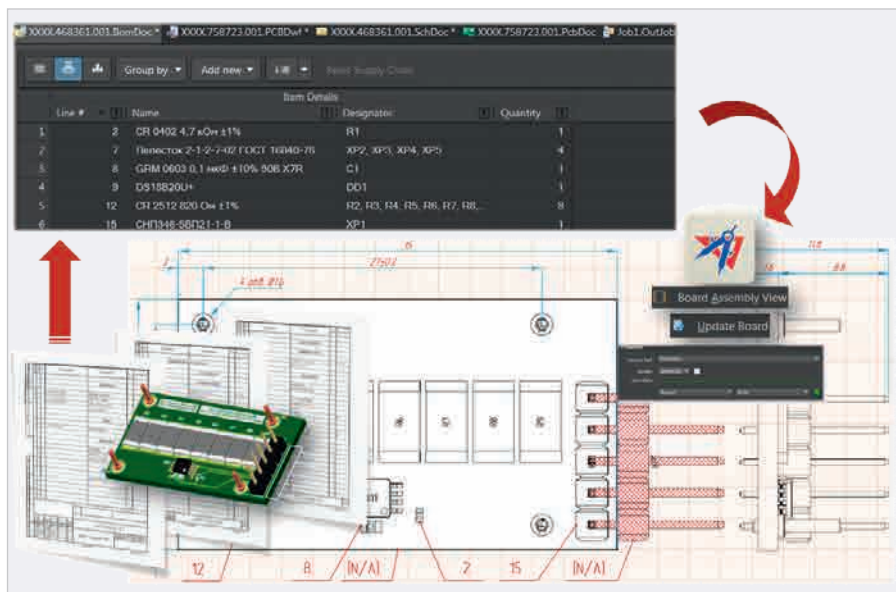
Добавление позиционных обозначений на сборочный чертёж
